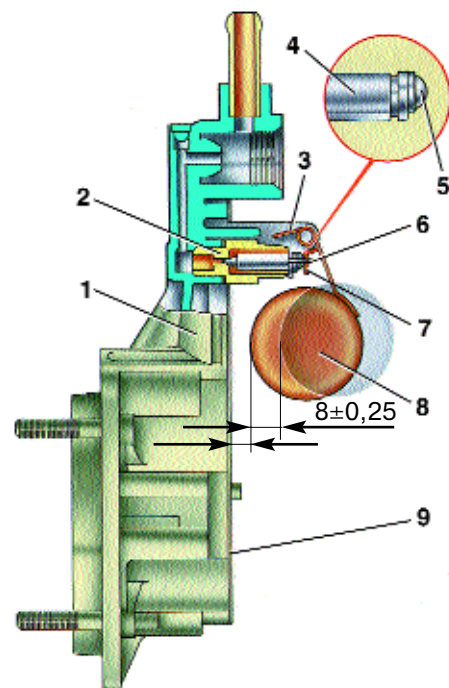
Регулировка уровня топлива в поплавковой камере карбюратора: 1 – крышка карбюратора; 2 – седло игельчатого клапана; 3 – упор; 4 – игельчатый клапан; 5 – шарик игельчатого клапана; 6 – оттяжная вилка игельчатого клапана; 7 – язычок рычага поплавка; 8 – поплавок; 9 – прокладка крышки карбюратора
